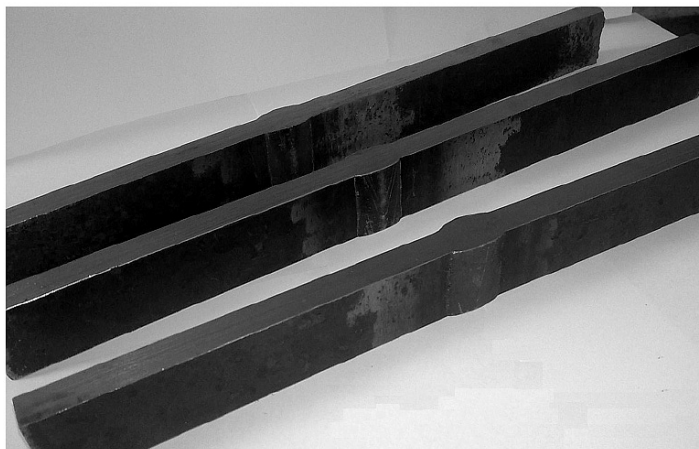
Общий вид образцов сварного стыкового соединения.
